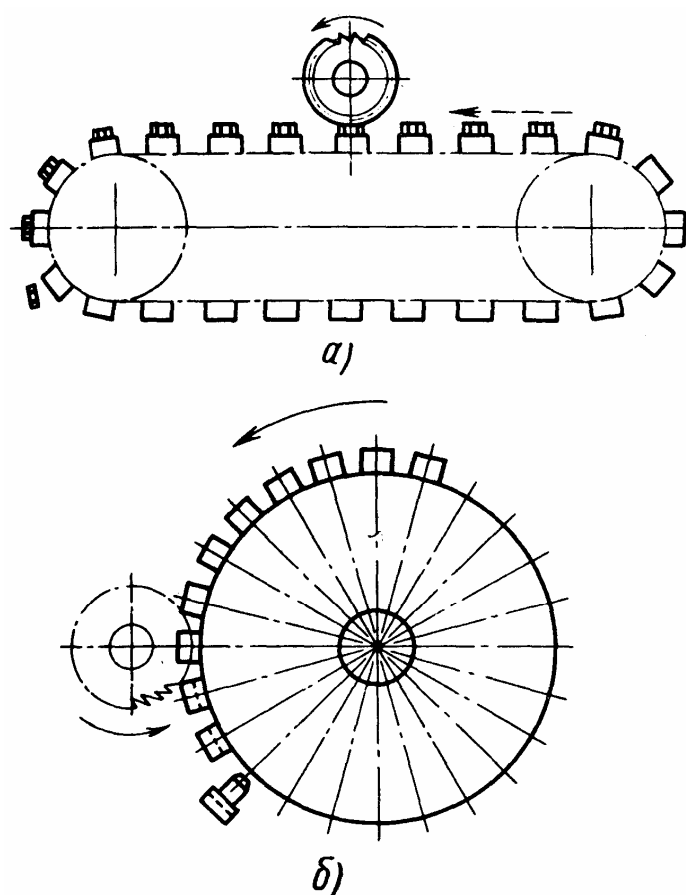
Пристосування до горизонтально-фрезерного верстата: а – конвеєрного типу; б – барабанного типу
